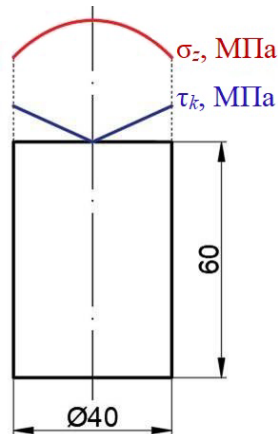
Предположительная эпюра нормальных и касательных контактных напряжений высокой заготовки
